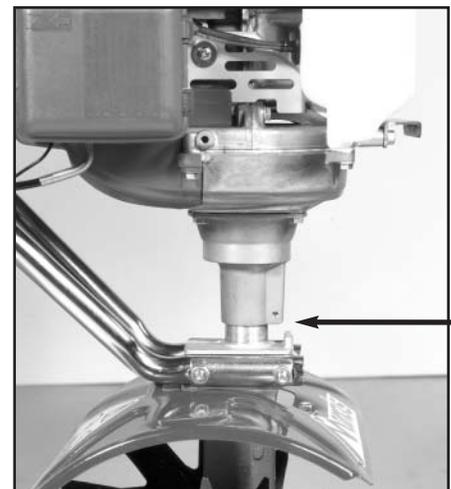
Der Motor liegt nicht richtig auf dem Getriebe auf.
